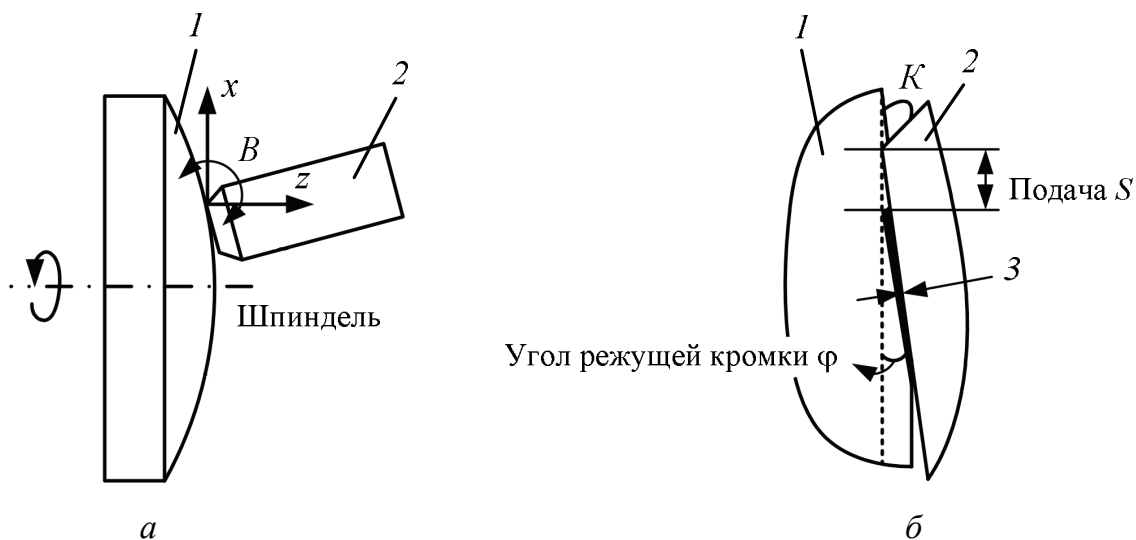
Схематическая модель обработки асферической поверхности инструментом с прямолинейной режущей кромкой:
